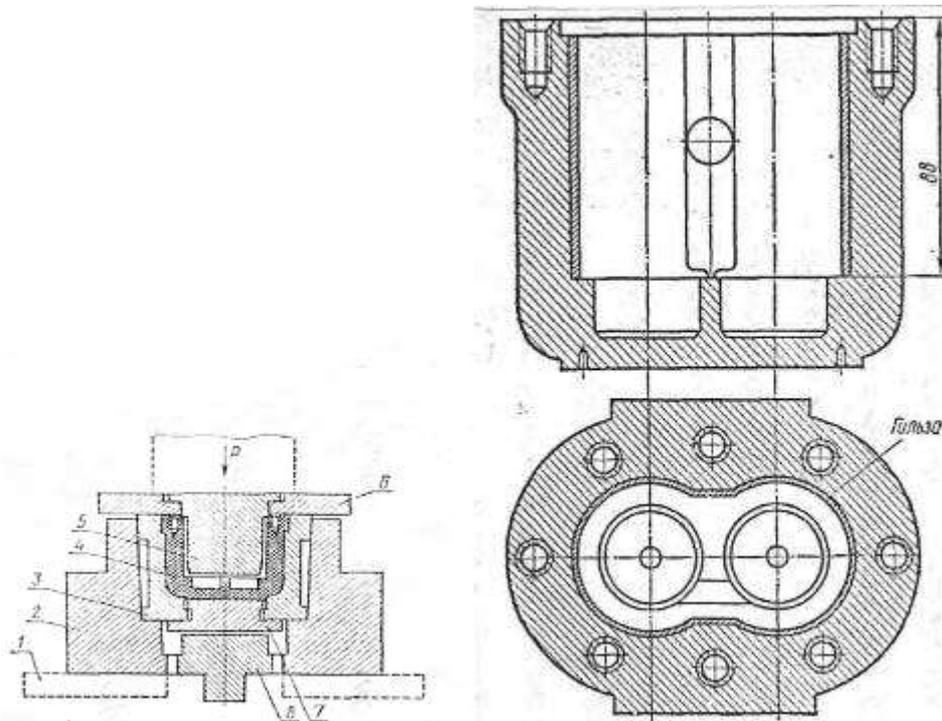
Приспособление для обжатия корпусов насосов:
